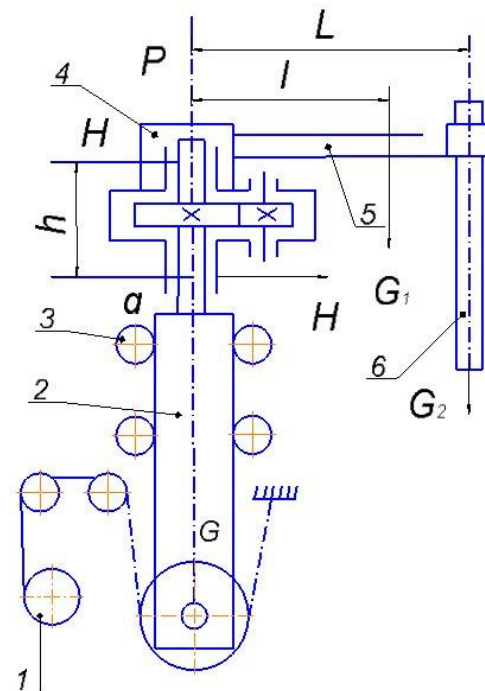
Принципова і розрахункова схеми фурменої установки:
